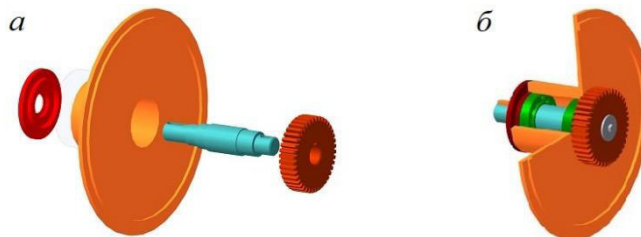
Моделі: а – деталей сонячного зубчастого колеса; б – їх зборка
